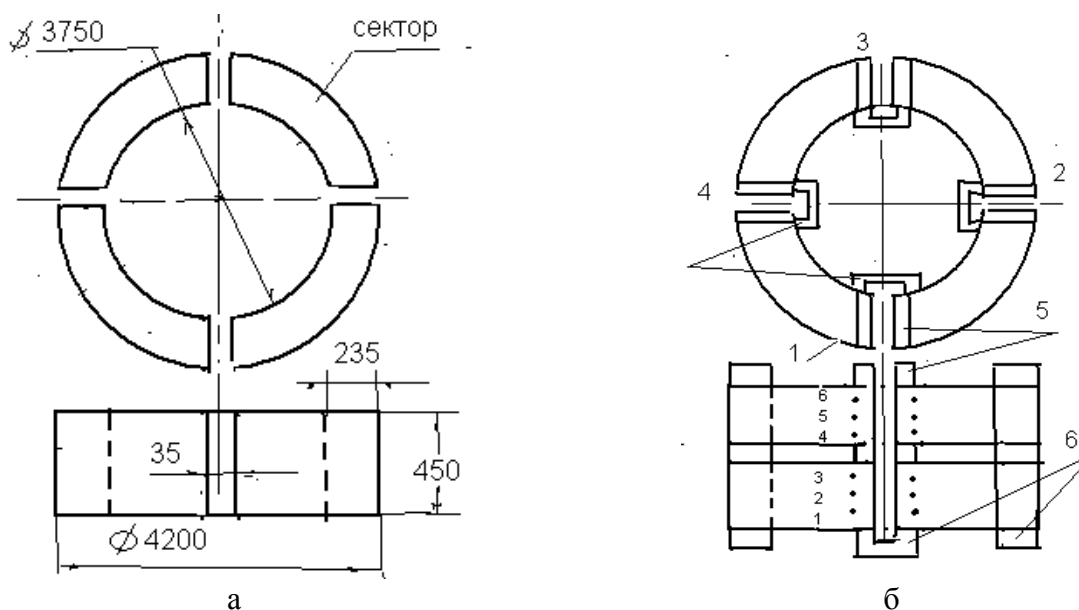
Общий вид бандажа (а) и схема сборки двух бандажей под электрошлаковую сварку (б).
